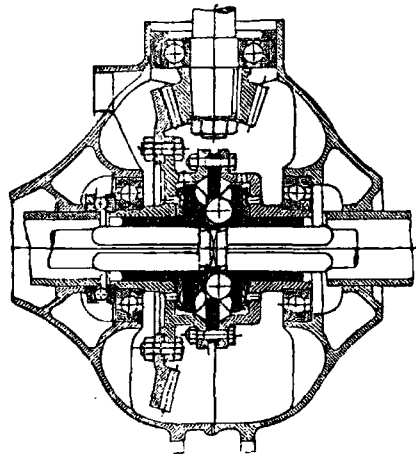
Дифференциал с цилиндрическими шестернями.
